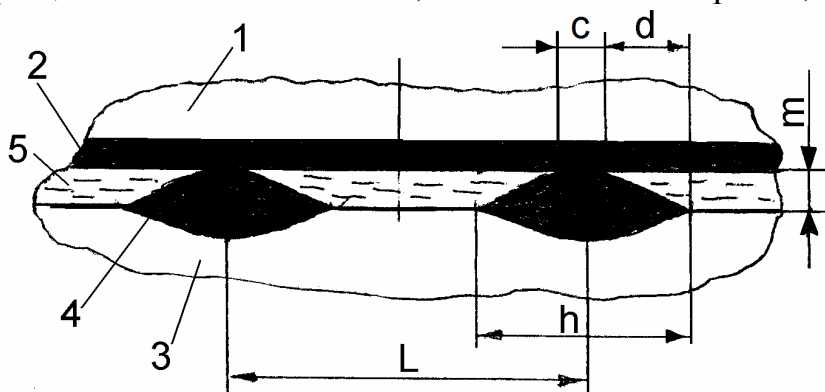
Схема расположения валиков при нереверсивной работе подшипника
